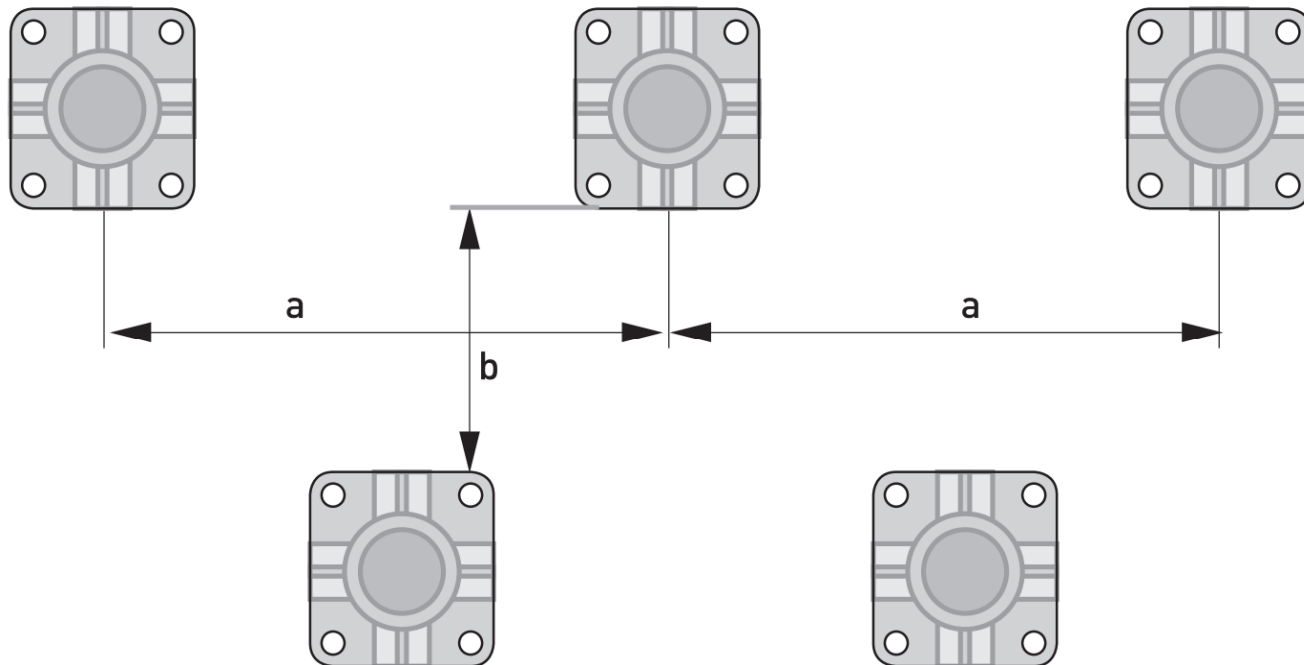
Крепление корпуса преобразователя сигналов раздельной версии
